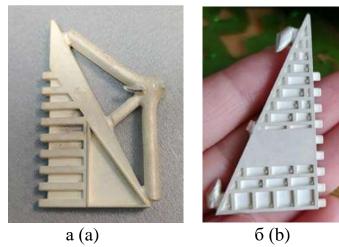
Литая необработанная заготовка для броши: а - вид спереди, б - вид сзади
